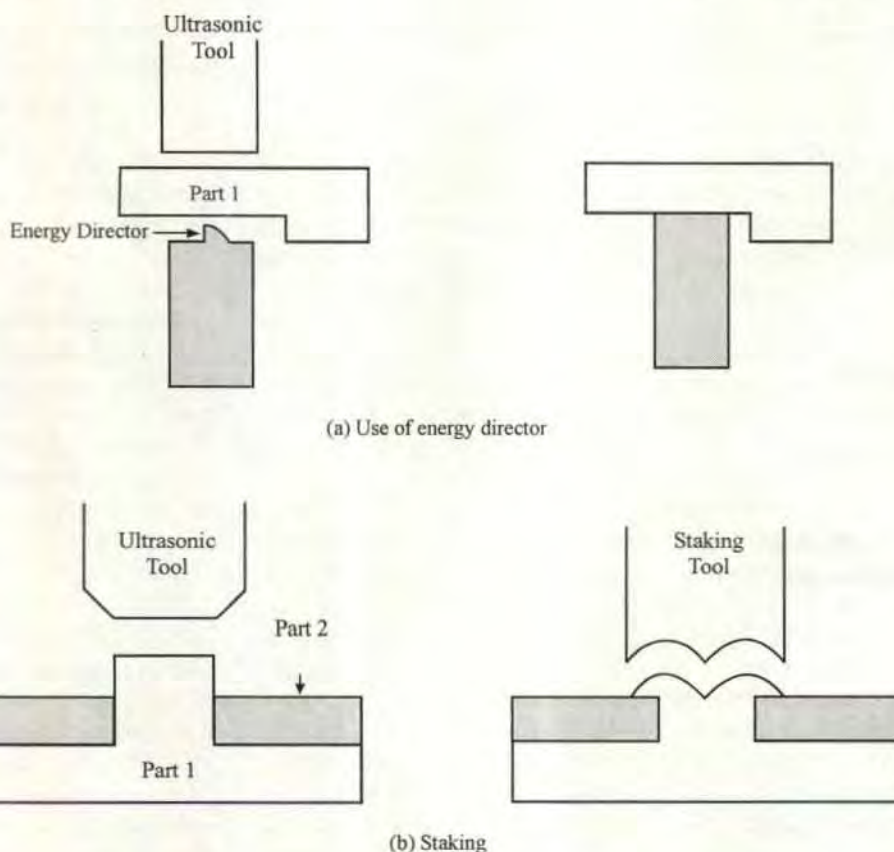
Soldadura ultrasónica que muestra (a) el uso de un director de energía para obtener una soldadura ultrasónica eficiente y (b) el principio de piqueteo
